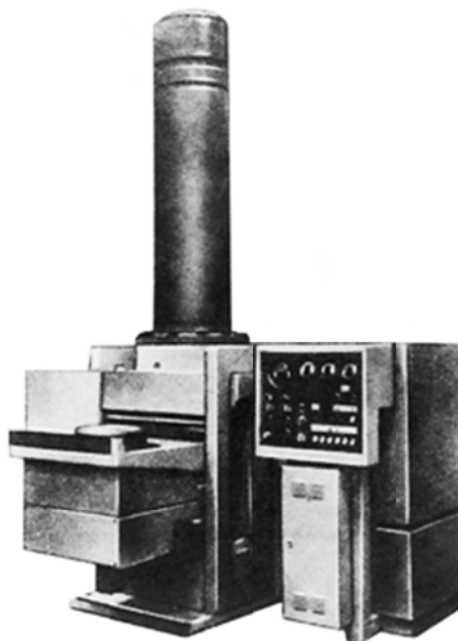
Установка для пневмоударной штамповки жидкостью модели T1324M
